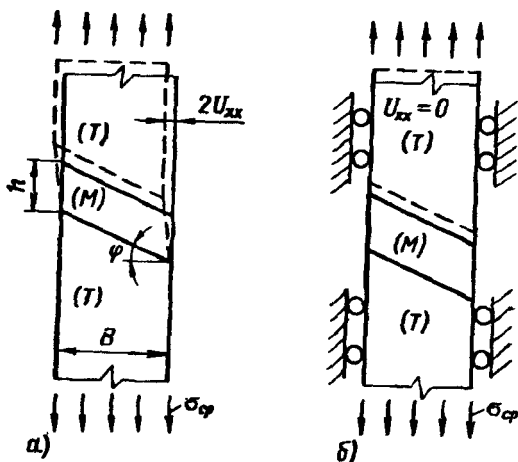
Схемы нагружения сварных соединений с косо мягкой прослойкой: а — “мягкая”; б — “жесткая”
